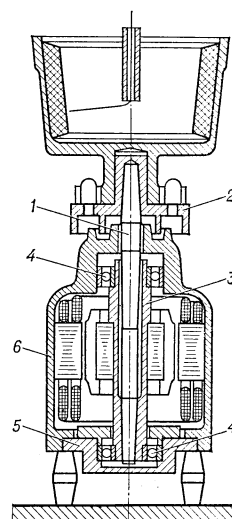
Электроверетено для формирования вискозных волокон: 1 — шпиндель; 2 — насадка; 3 — втулка; 4 — шарикоподшипники; 5 — стакан; 6 — корпус.
